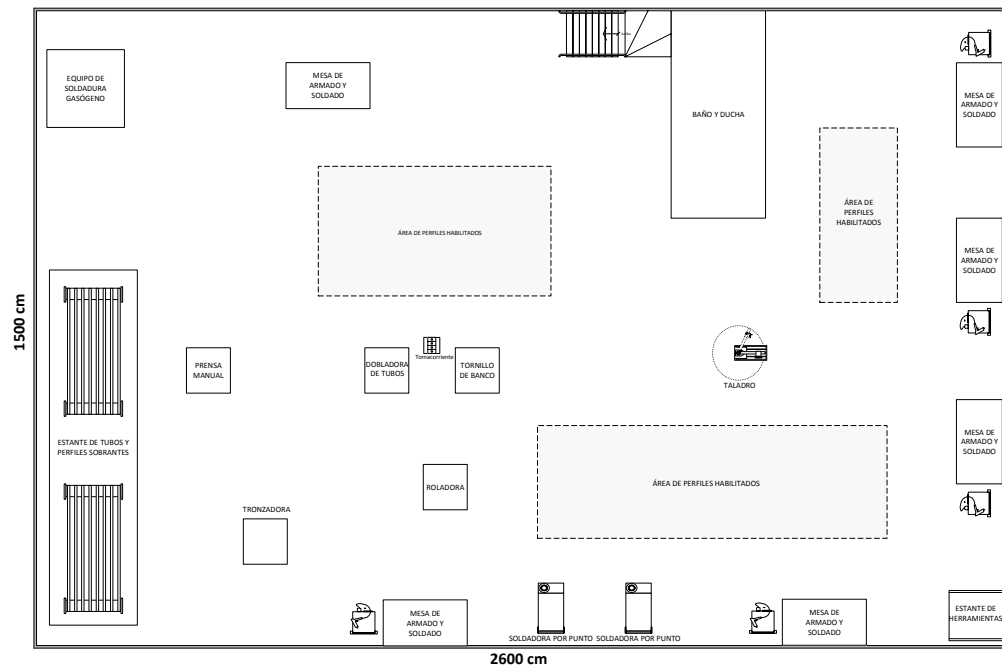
Distribución de la planta nivel 2 de la empresa Solisgas SAC.
